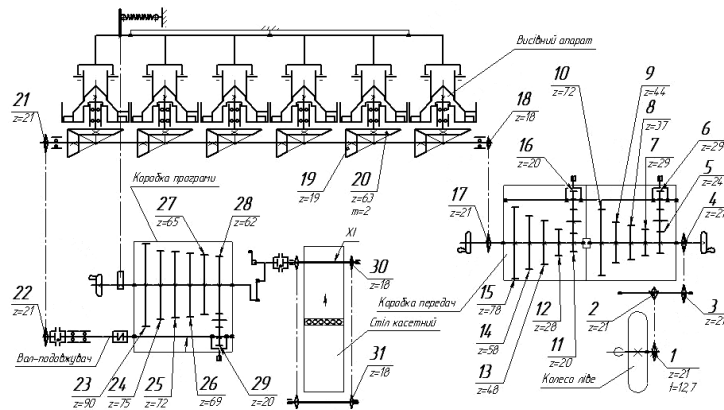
Схема кінематична сівалки навісної селекційної касетної СНСК-6 для II етапу :1-2, 3-4, 17-18, 21-22, 30-31– ланцюгові передачі; 5-6, 11-16, 28-29 – зубчасті передачі; 7-10, 12-15 – шестерні коробки передач; 19-20 – конічно-трибова передача; 23-27 – шестерні коробки програми
